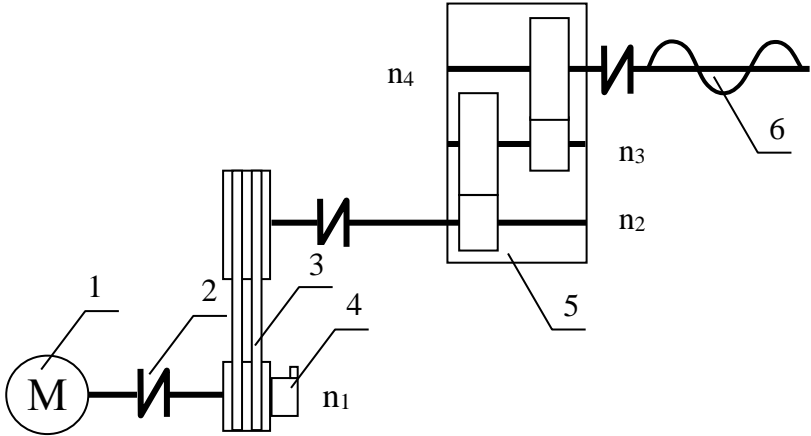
Кінематична схема приводу текстуратора із механічним регулюванням: 1 – електродвигун; 2 – муфта; 3 – клинопасова передача; 4 – варіатор; 5 – редуктор; 6 – шнек
